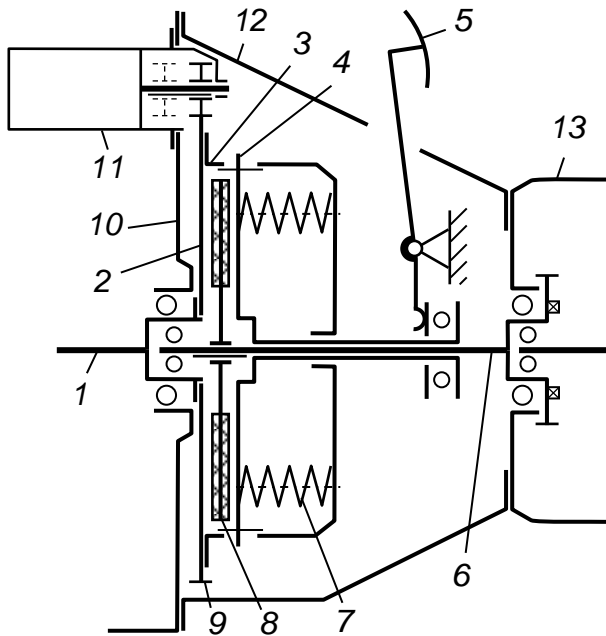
Кинематическая схема фрикционного однодискового сцепления с периферийно расположенными пружинами
